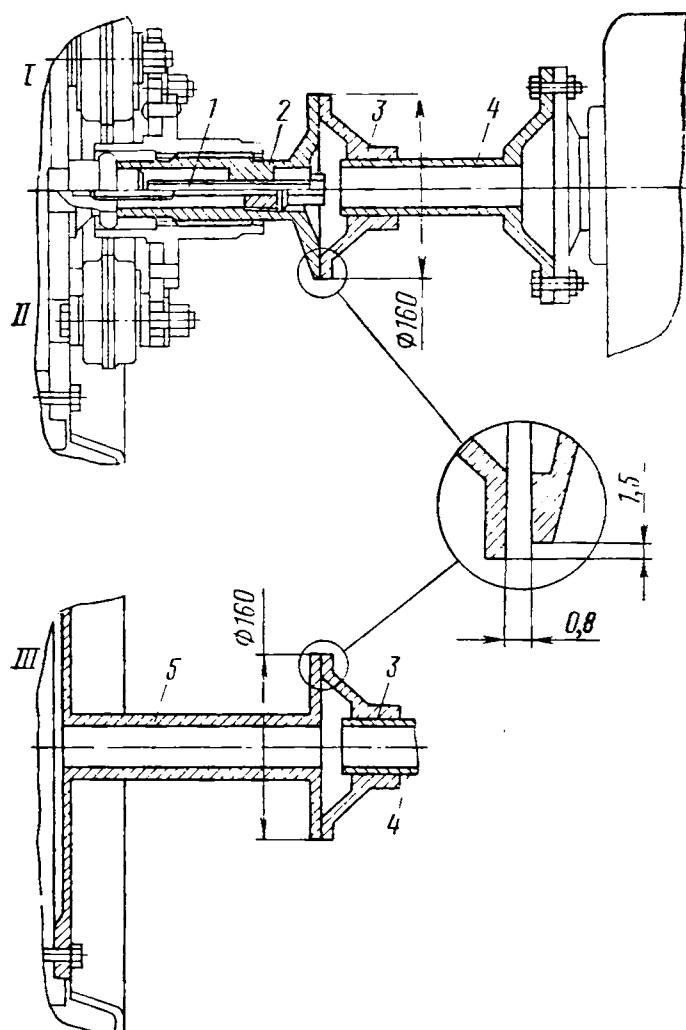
Центрирование гидромеханической передачи с двигателем:
